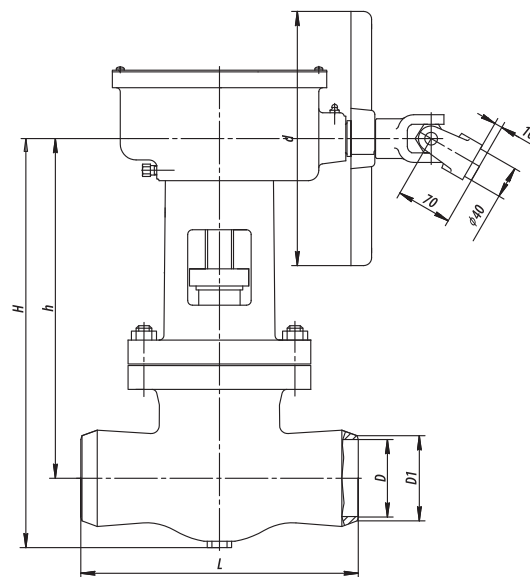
Задвижка DN80-100 с коническим редуктором
